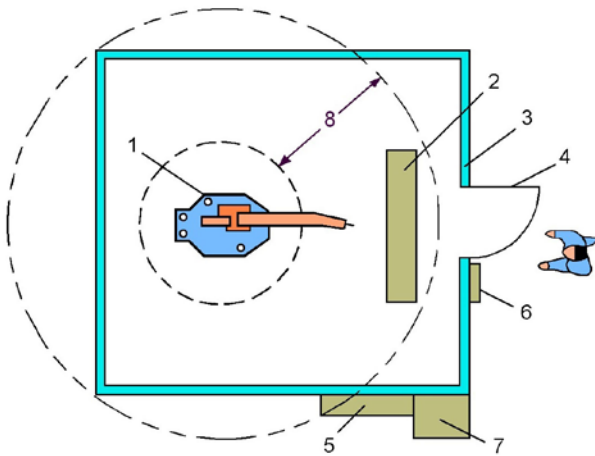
Schweißzelle mit manueller Eingabe und Entnahme der Schweißteile.
